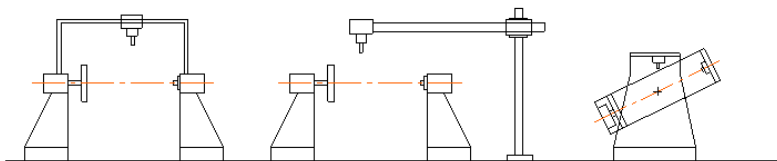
Схемы установок для сварки круговых швов поверхностей изделий, закрепленных в центрах на опорах
